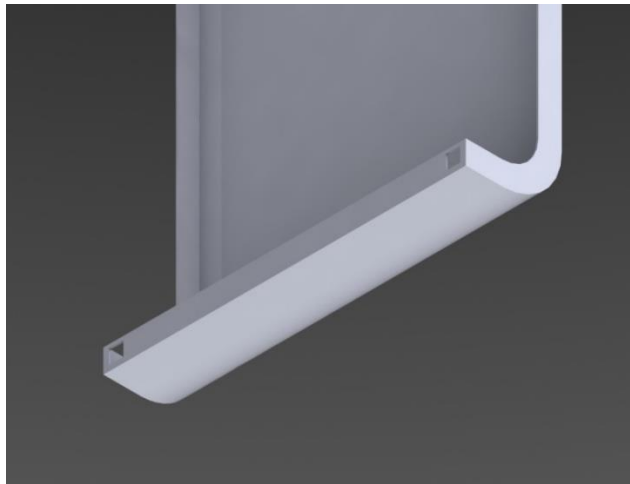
Ensamblaje subconjunto 1.1. Soldadura 8.
